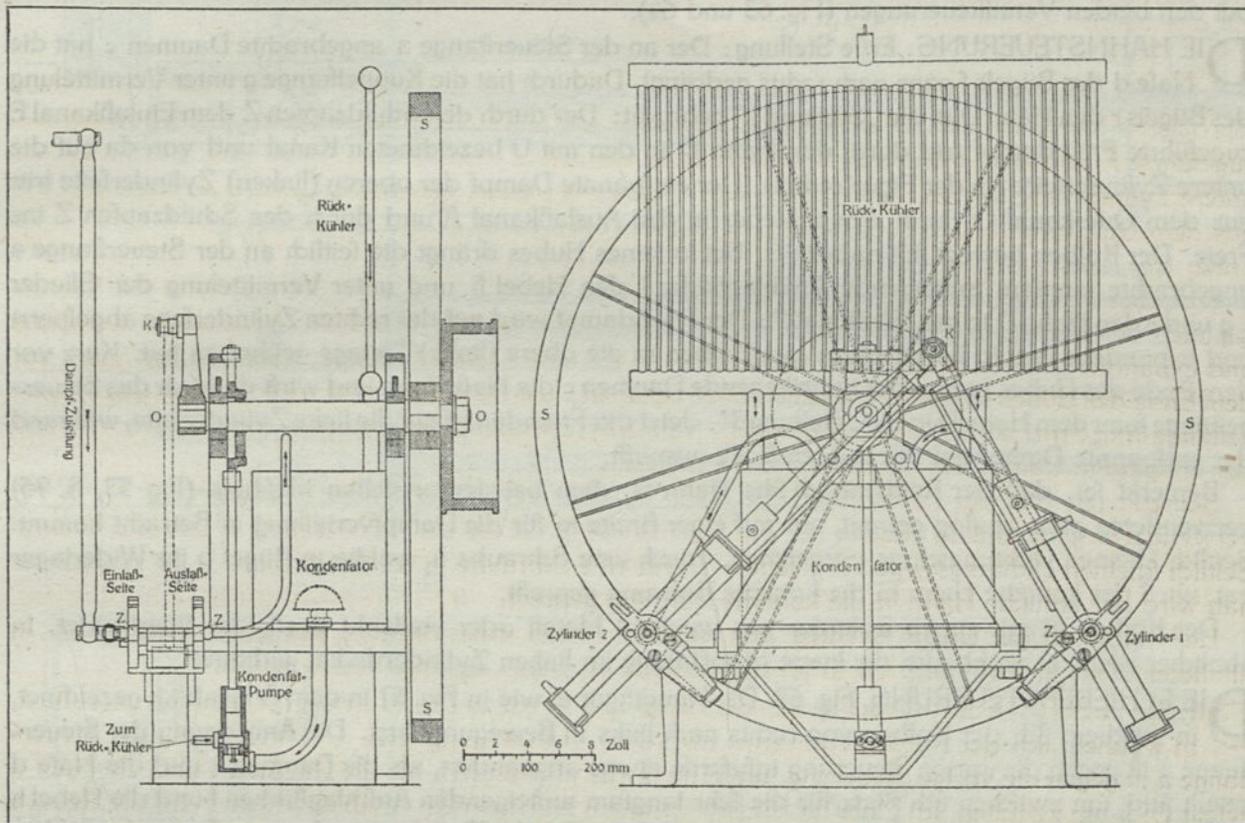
Entwurf einer Zwillingsmaschine mit oszillierenden Zylindern und Rückkühler.
